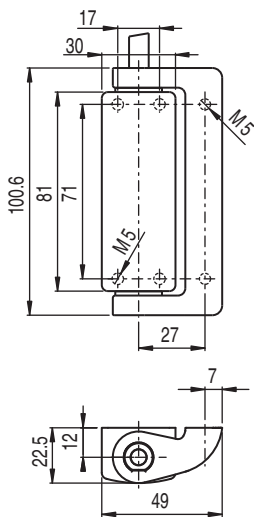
Dimensiones S400-M4CB2-T en mm
